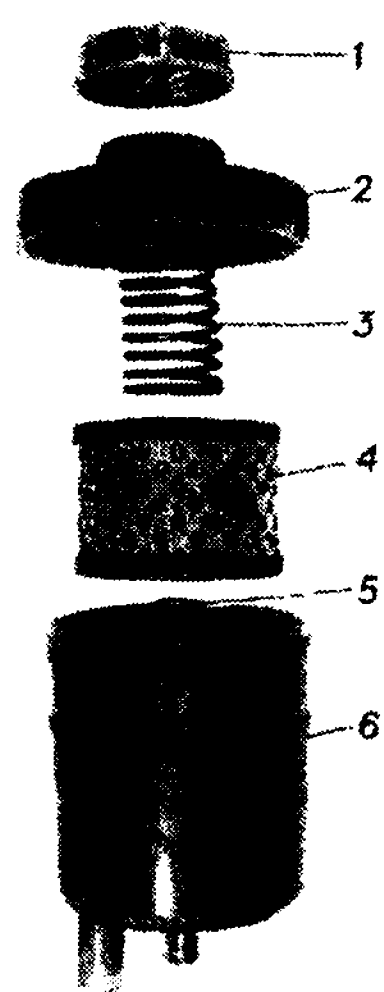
Бачок ШНКФ 453473.400 системы ГУР: 1 - пробка; 2 - крышка; 3 - пружина; 4 - фильтрующий элемент; 5 - уплотнительное кольцо; 6 - корпус бачка
